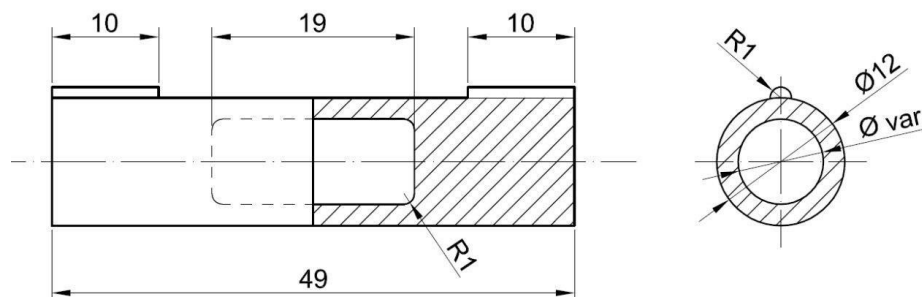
Vista de alzado y perfil de probeta hueca para ensayo a torsión en equipo manual
